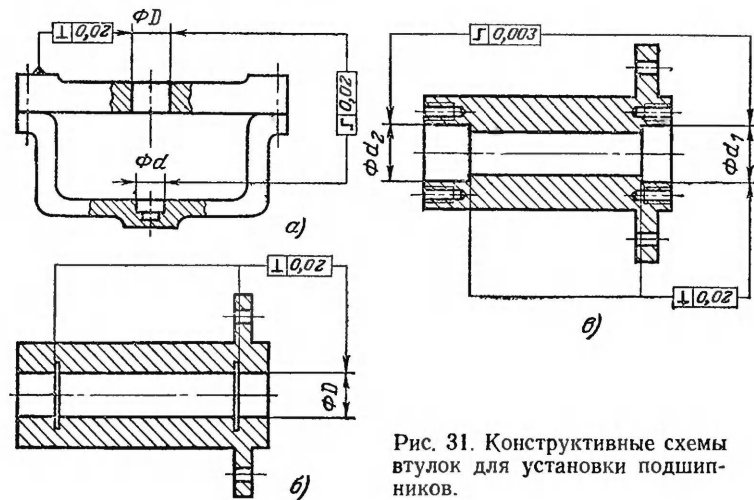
Конструктивные схемы втулок для установки подшипников.
